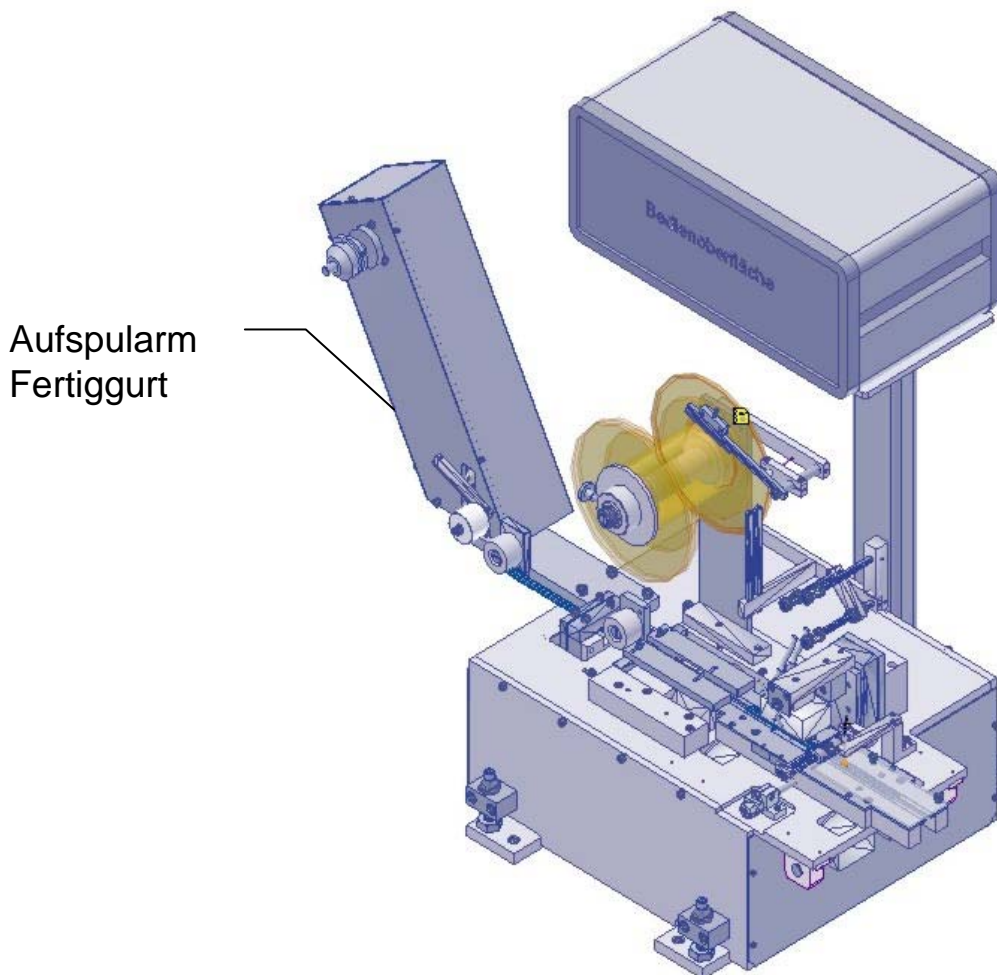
CAV-2 Modul mit Laufrichtung rechts-links
